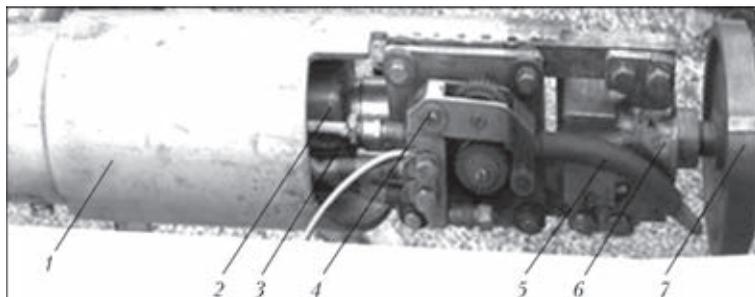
Автомат для сварки в стесненных условиях на большой глубине: 1 — корпус; 2 — механизм вращения; 3 — направляющий канал; 4 — подающий механизм с колебателем мундштука; 5 — мундштук; 6 — крепление и элементы токопередачи на доньшко; 7 — доньшко
